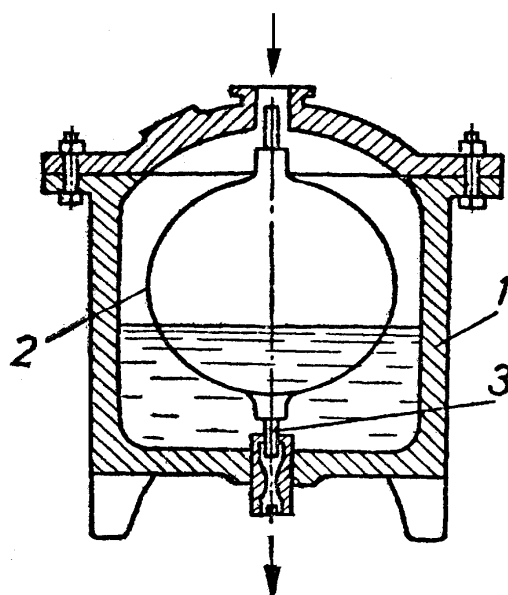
Конденсатоотводчик с закрытым шаровым поплавком для повышенного давления: 1 – корпус; 2 – поплавок; 3 – клапан
